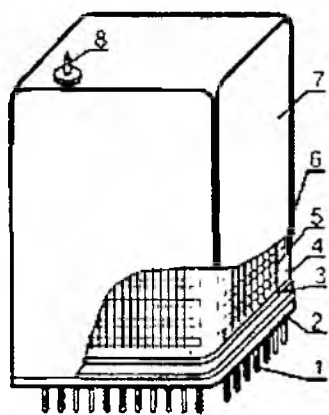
Конструкція етажерочного мікроблоку ТС: 1 – контакти з ковару; 2 – основа; 3 – перехідна комутаційна друкована плата з фотосеталу; 4 – стійка; 5 – мідні комутаційні шини; 6 – мікроплати; 7 – термокожух; 8 – штенгель для заповнення інертним газом
